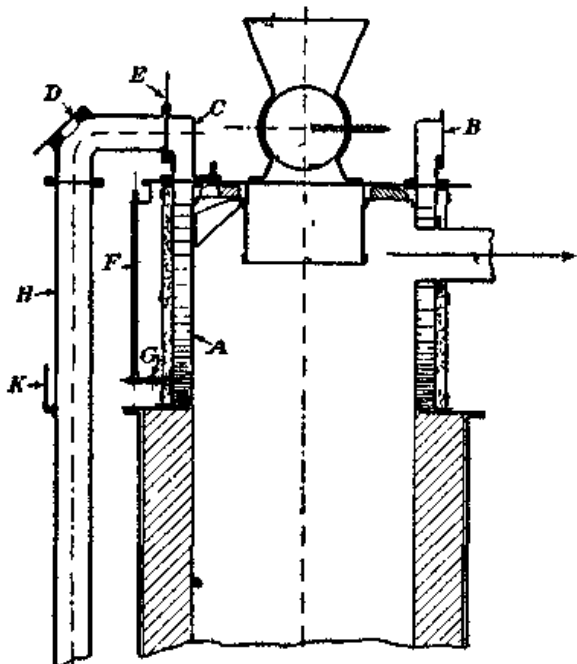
Всасывающий генератор Пауэр Газ Корпорейшен с испарителем.
